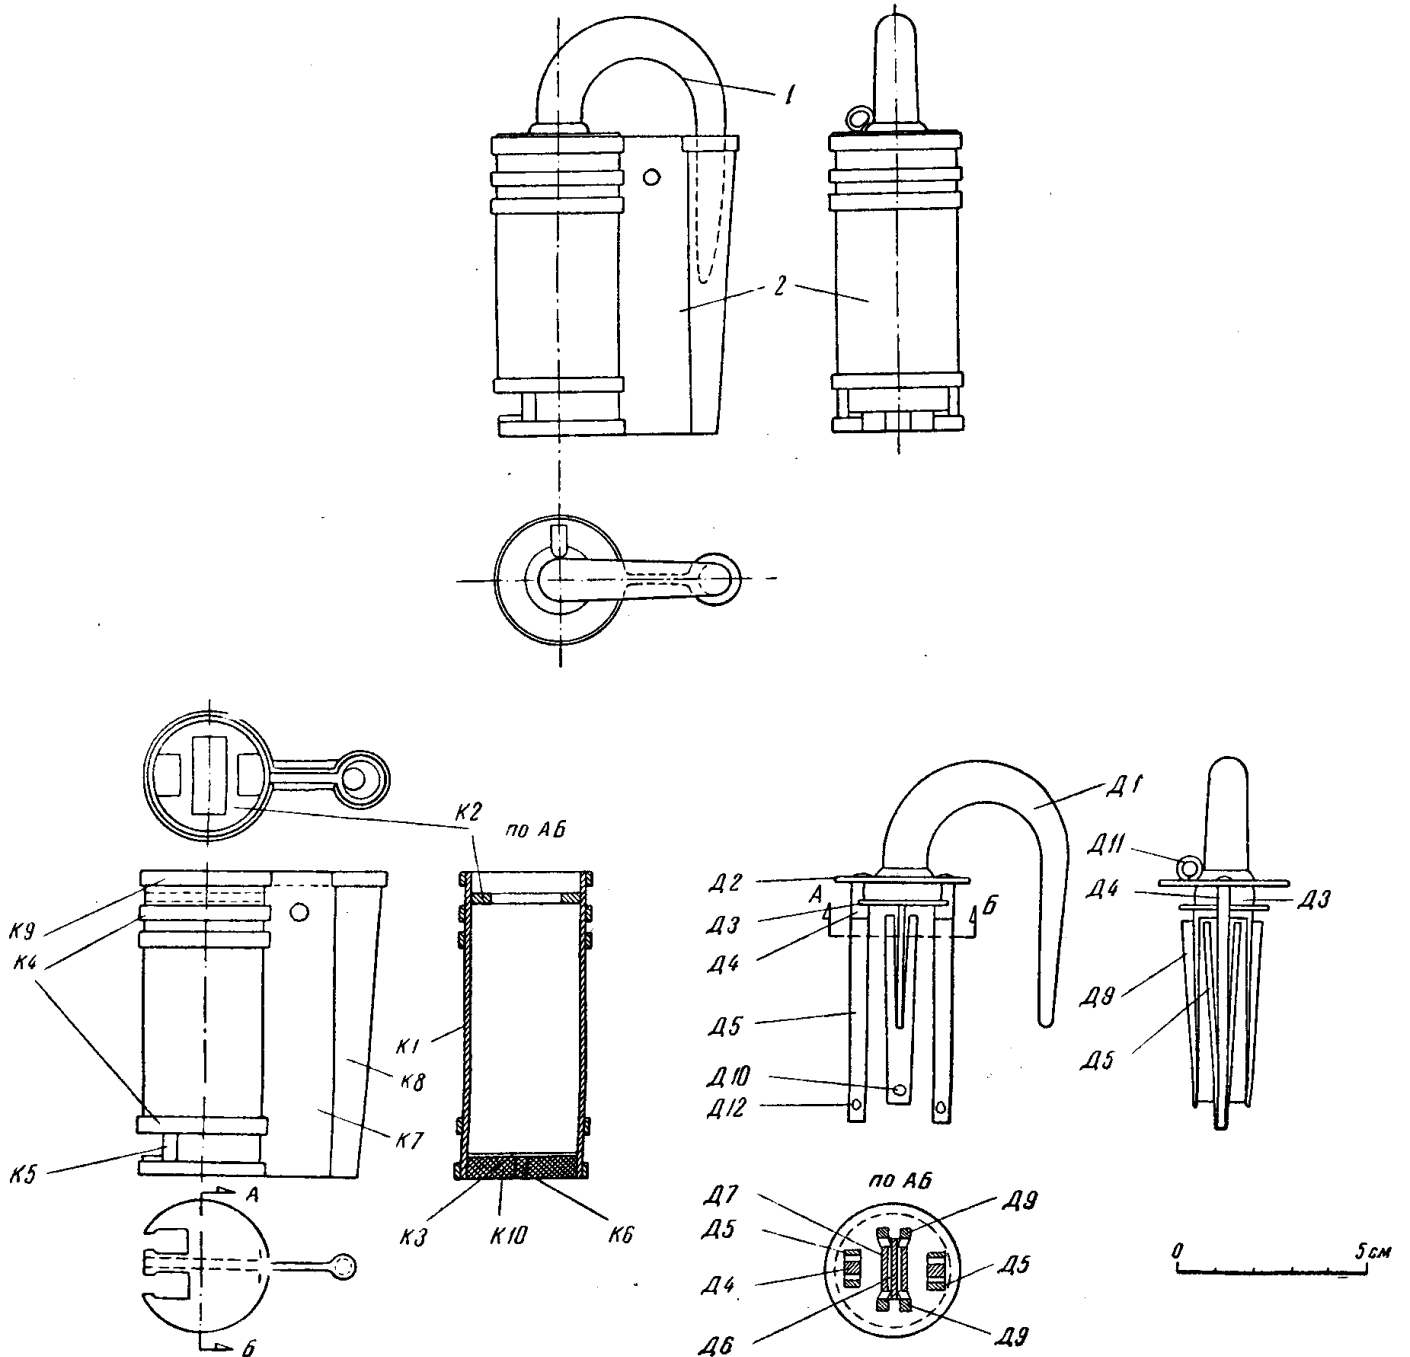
Устройство цилиндрического пружинного замка (Княжая Гора)
